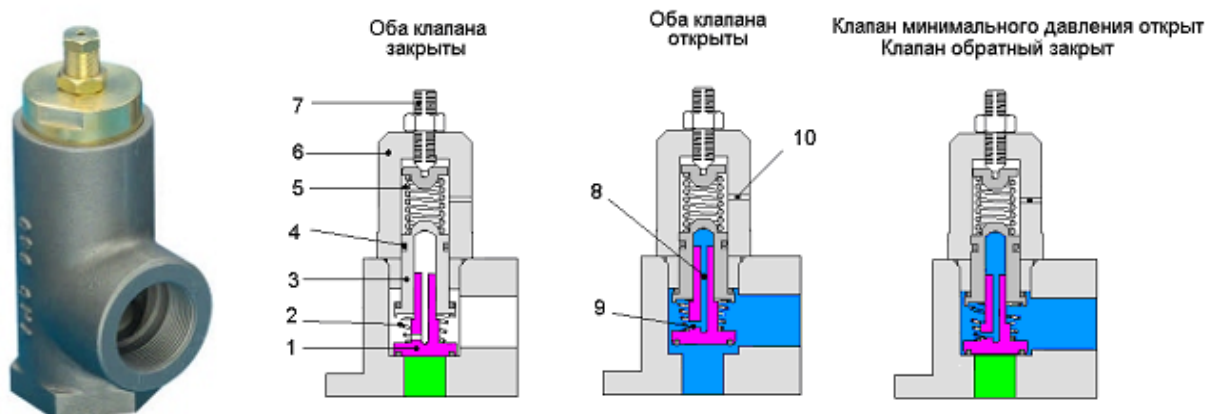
Клапан минимального давления типа: 1 – тарелка обратного клапана; 2 – пружина обратного клапана; 3 – поршень клапана минимального давления; 4 - кольцо уплотнительное; 5 – пружина клапана минимального давления; 6 – корпус (цилиндр поршня); 7 – винт регулировочный; 8 – канал осевой; 9 – канал радиальный; 10 – отверстие дренажное.
